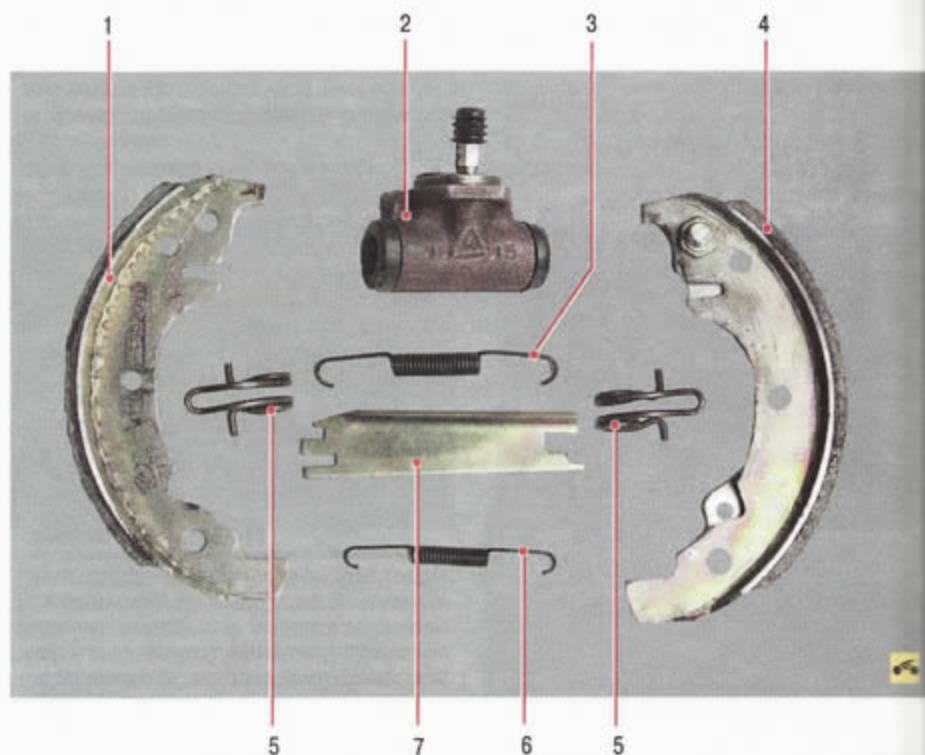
Детали тормозного механизма заднего колеса (показаны детали тормозного механизма с левой стороны): 1 – передняя тормозная колодка; 2 – рабочий цилиндр; 3 – верхняя стяжная пружина; 4 – задняя тормозная колодка с разжимным рычагом привода стояночного тормоза; 5 – прижимная пружина; 6 – нижняя стяжная пружина; 7 – распорная планка
